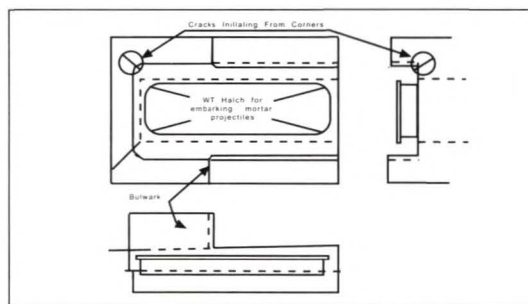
Agrietamiento en aberturas de cubierta en destructores clase Whitby.
